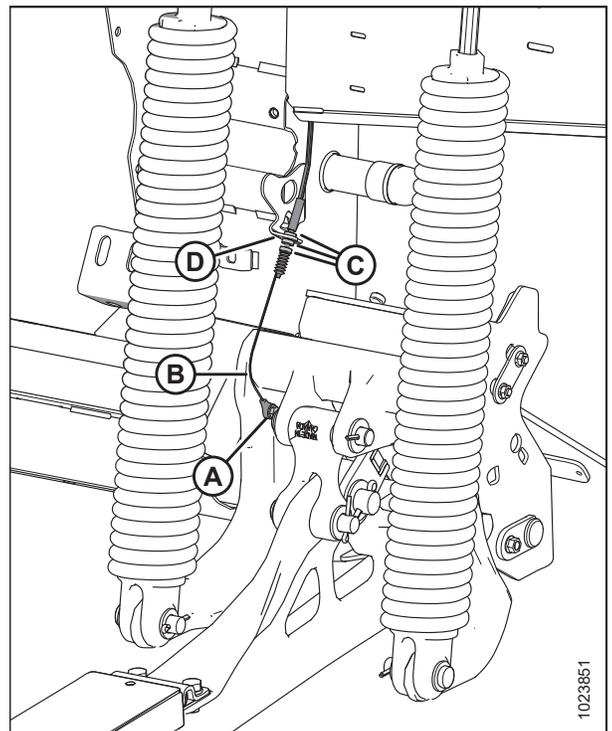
Lado dianteiro esquerdo de Adaptador de flutuação – O lado dianteiro direito é o lado oposto
